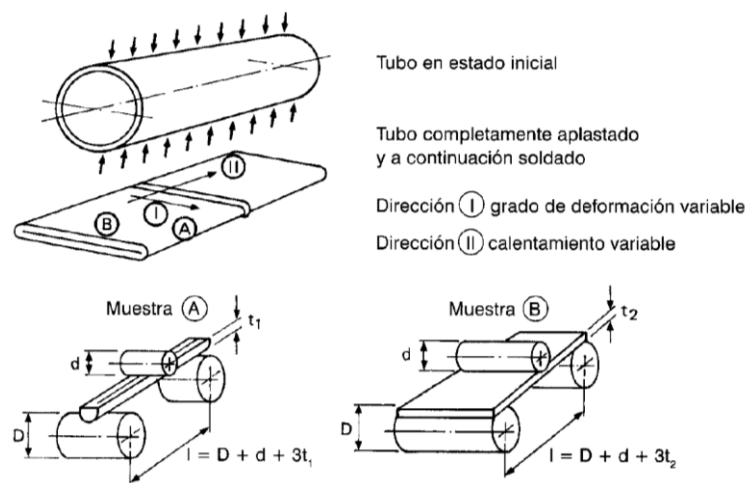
Possible fissuració en extrems aplanats de perfils tubulars.
